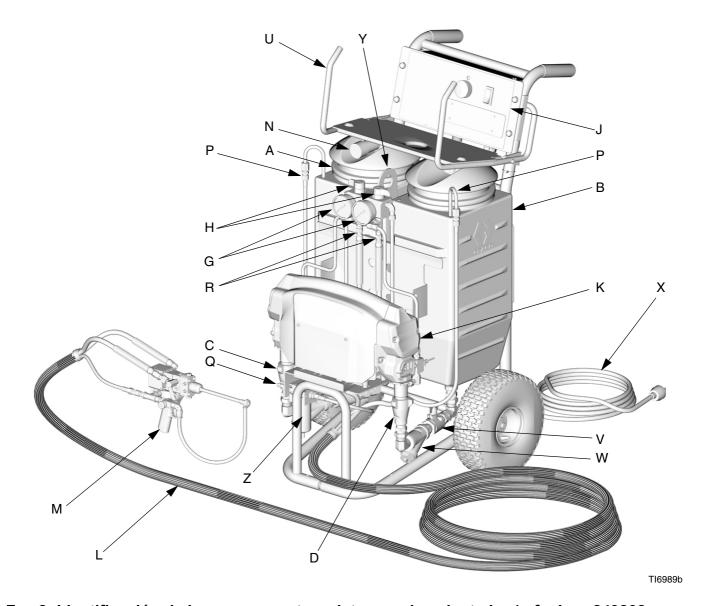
Identificación de los componentes, sistemas sin calentador (ref. pieza 249808 representada)
